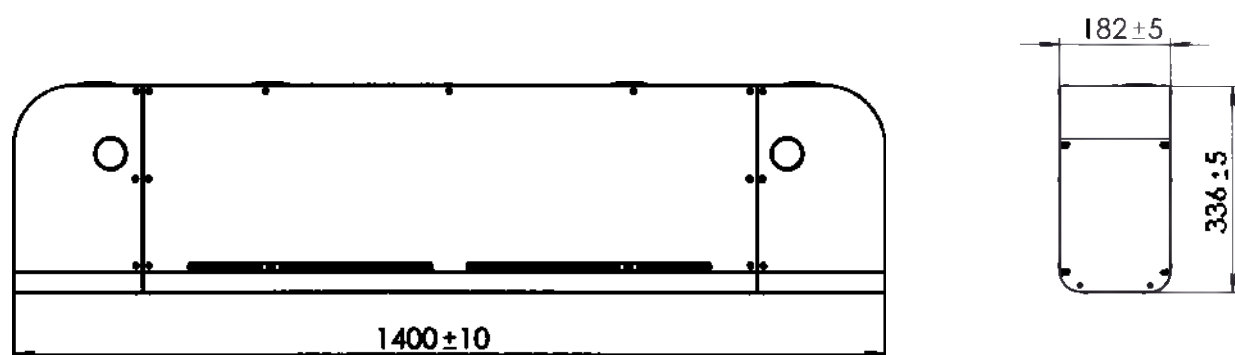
Модуль с двумя исполнительными механизмами.
